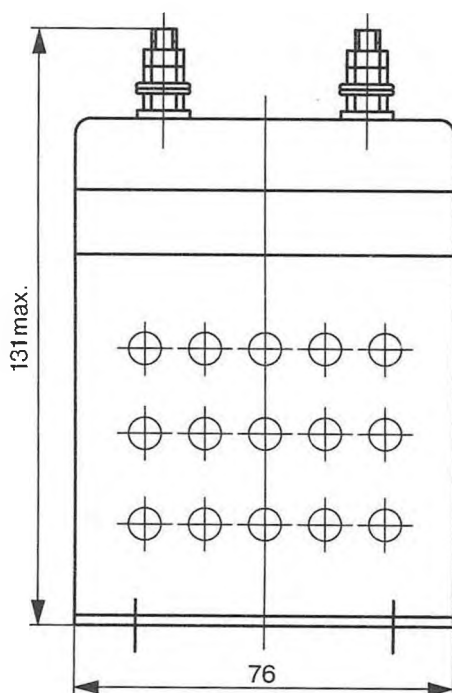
Габаритные и установочные размеры блока конденсаторного КБД-6
